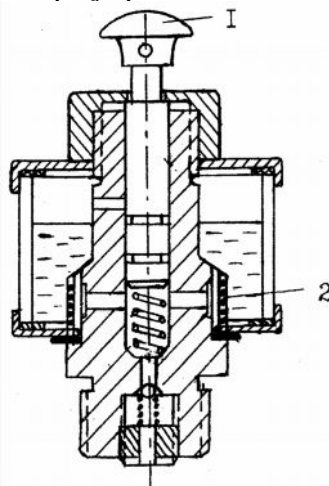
Одноплунжерний маслянка з резервуаром:
